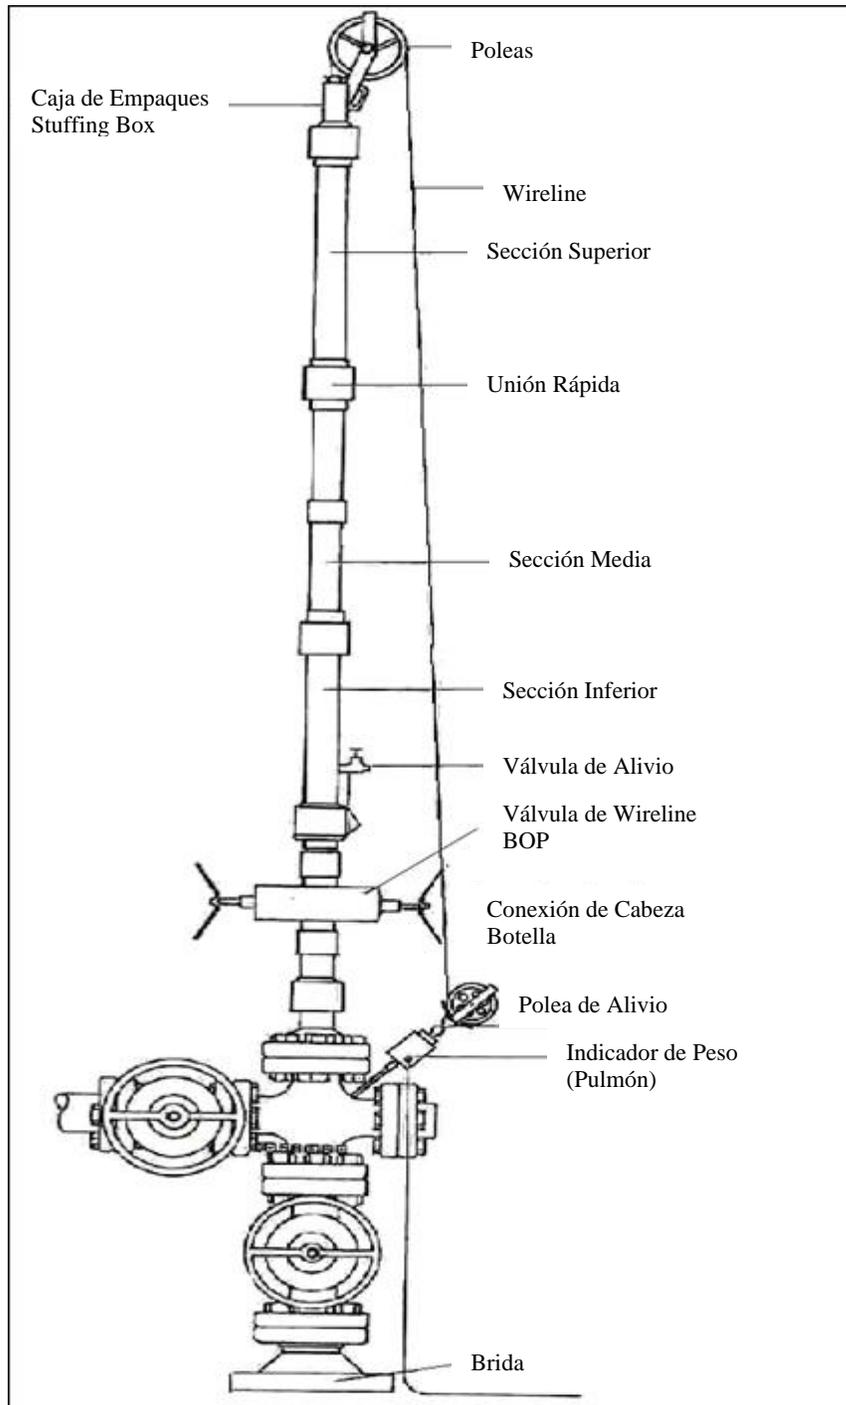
Partes y Montaje del Lubricador y el equipo de superficie.
